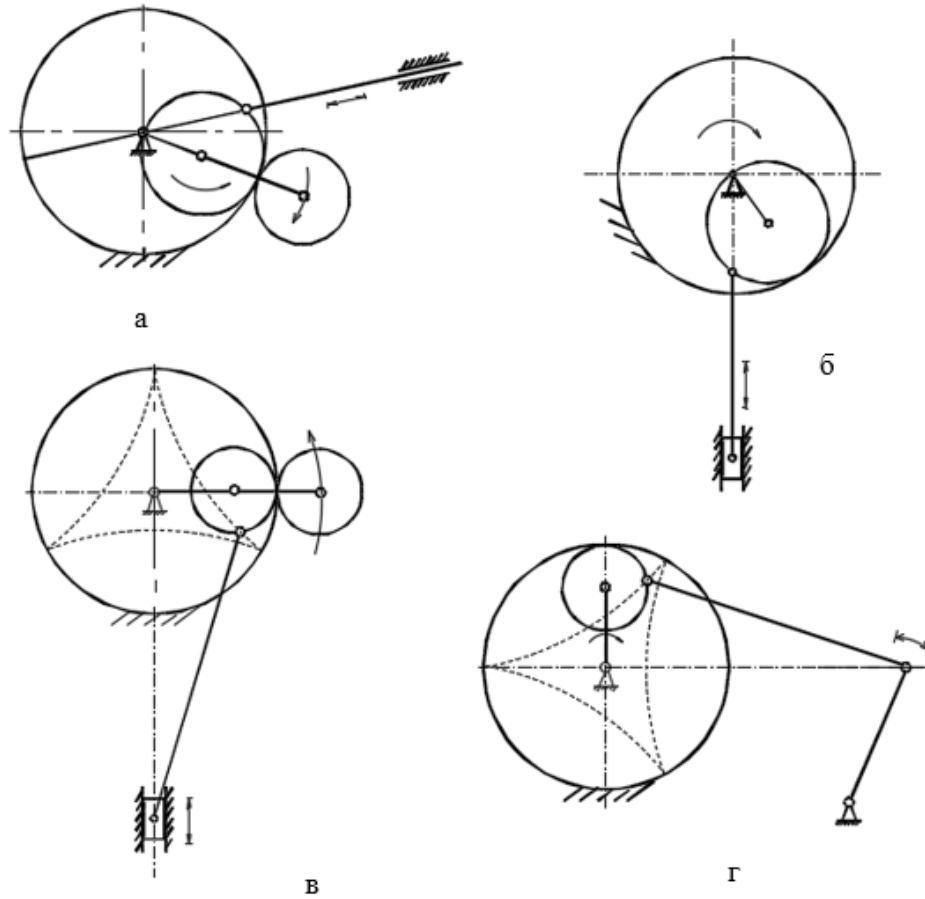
Зубчато-важільні планетарні механізми: а - направляючий механізм; б - направляючий механізм преса; в - механізм з зупинкою вихідної ланки; г - механізм з зупинкою коромисла
